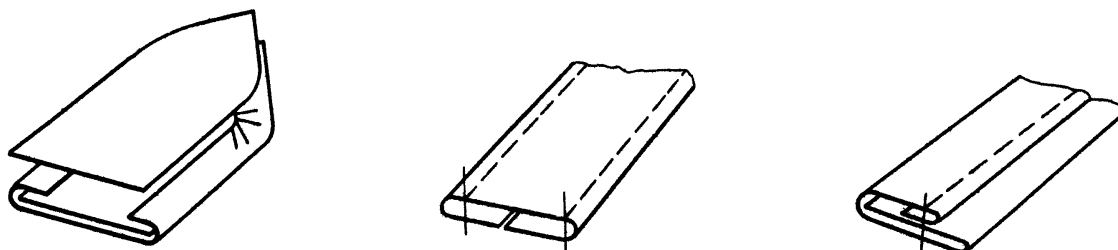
Схема сборки корпуса сумки выворотным
